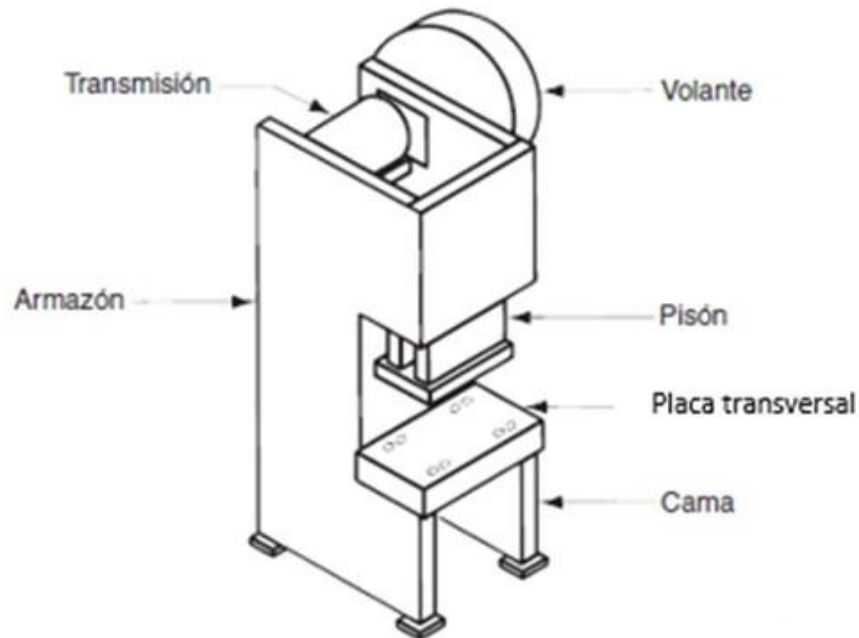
Componentes de una prensa troqueladora accionada por una transmisión mecánica [1].
